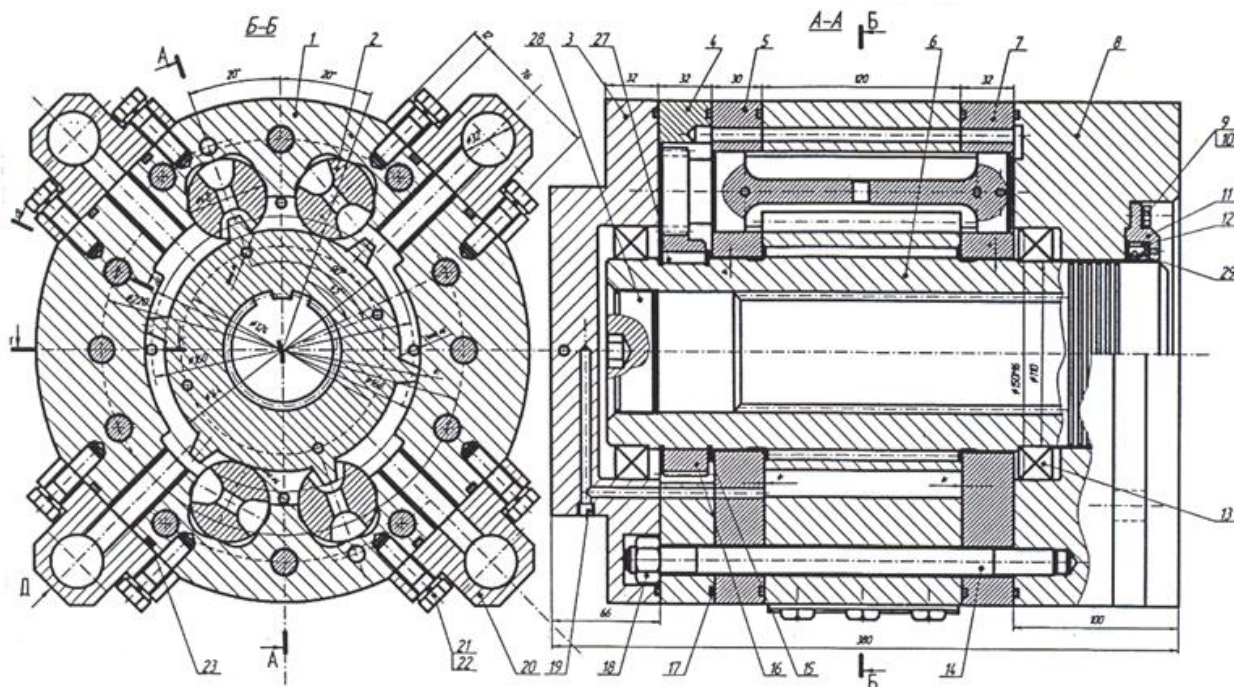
Высокомоментный гидромотор роliko-лопастного типа конструкции УГТУ–УПИ
